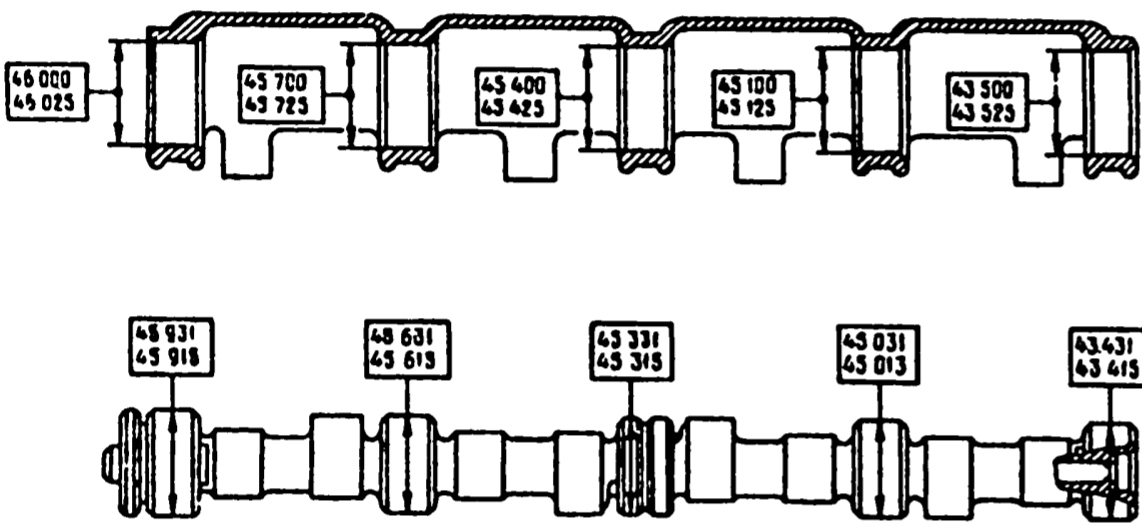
Основные размеры распределительного вала и расточек в корпусе подшипников распределительного вала
